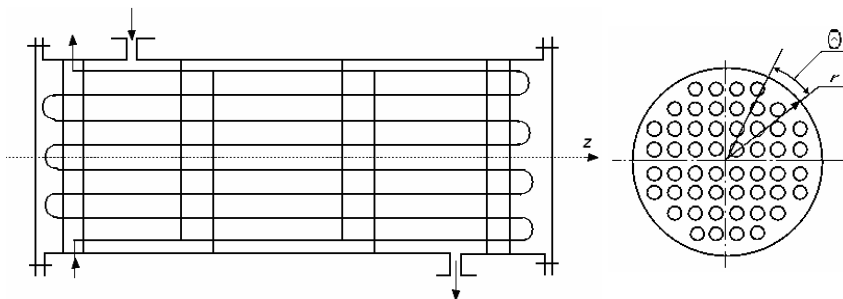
Схема типовой конструкции кожухотрубного аппарата
